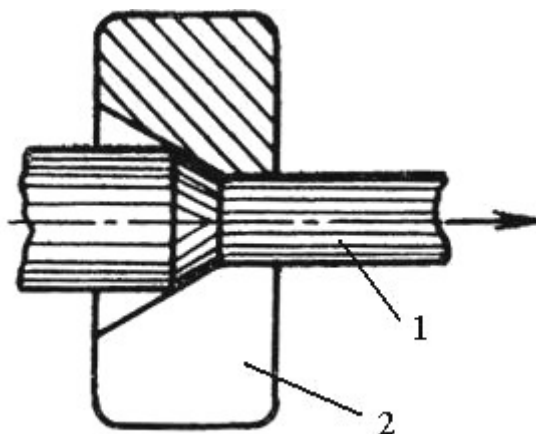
Схема процесса волочения: 1 – заготовка; 2 – волока
